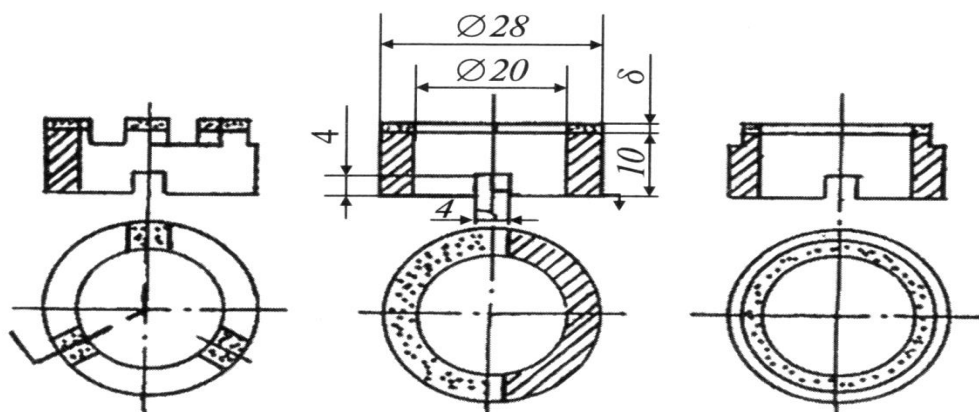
Образцы для испытаний покрытий на сухое трение
